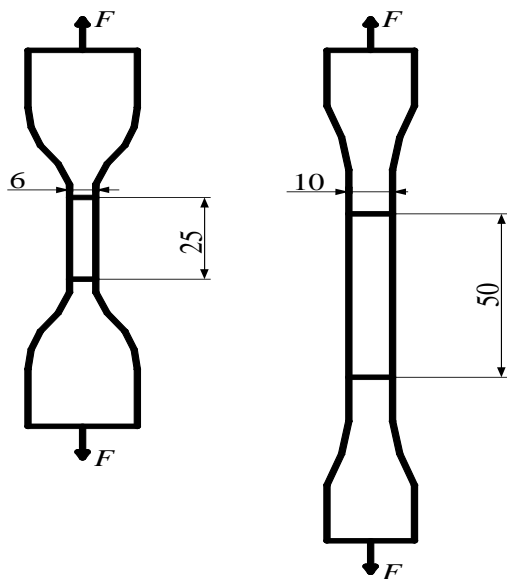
Тип образца из полиэтилена для испытания на устойчивость к разрыву
